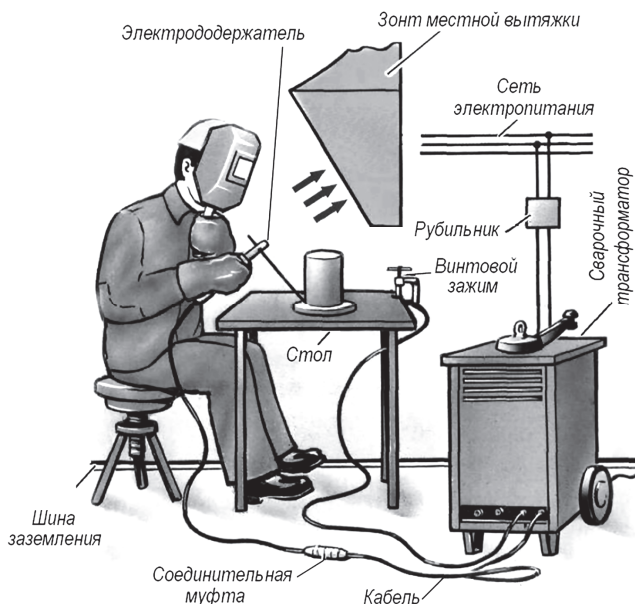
Рабочее место сварщика ручной дуговой сварки
